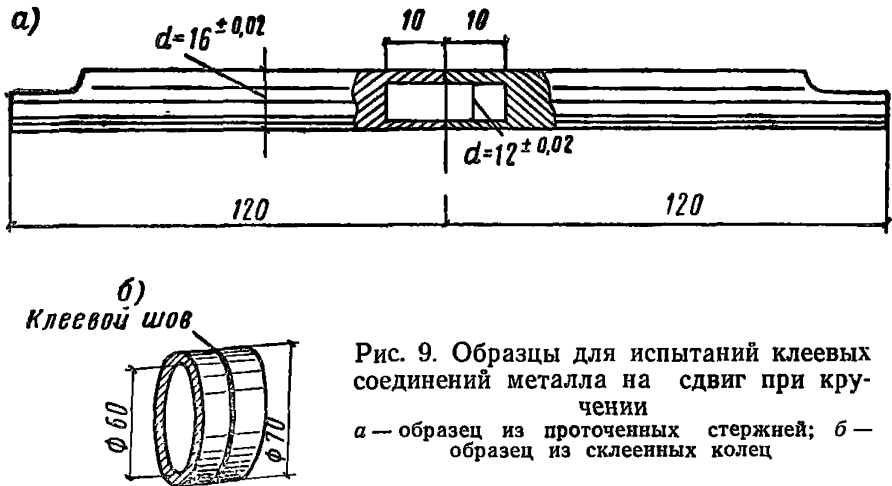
Образцы для испытаний клеевых соединений металла на сдвиг при кручении
